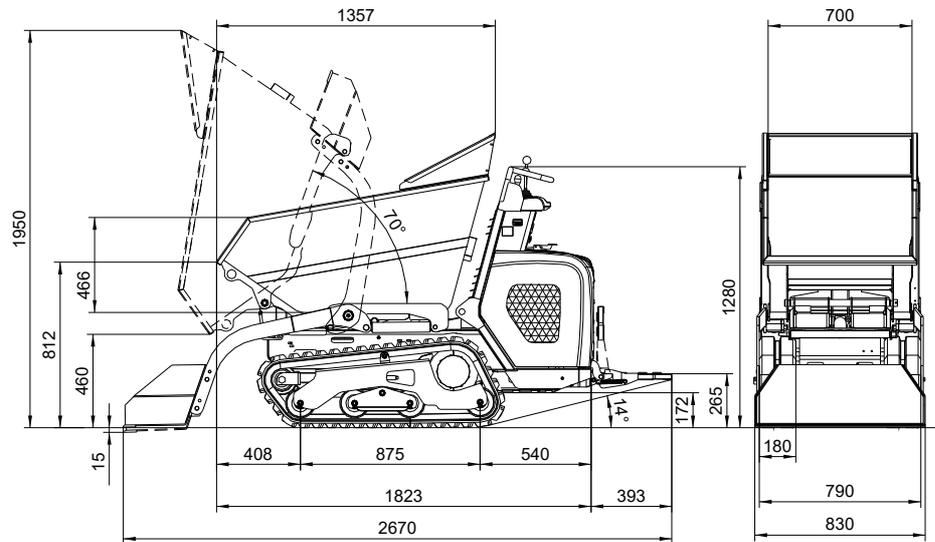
Fahrzeugabmessungen (Typ DT10 mit Kippmulde für leichtes Material)
